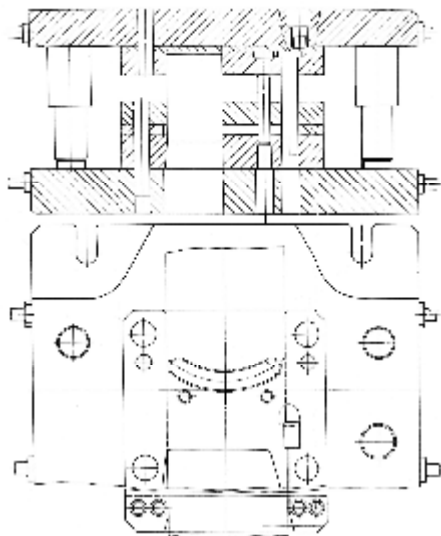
Штамп для изготовления деталей на ОАО «Кредмаш»
